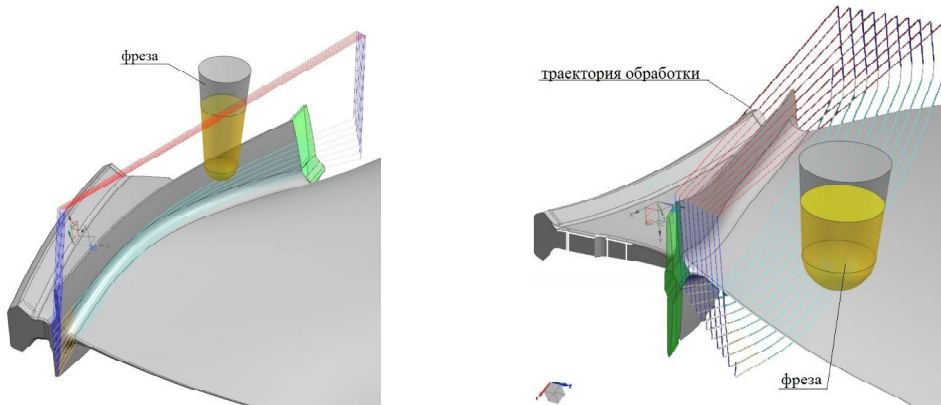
Фрезерование прикорневого участка пера лопатки на станке с ЧПУ ФП-17
